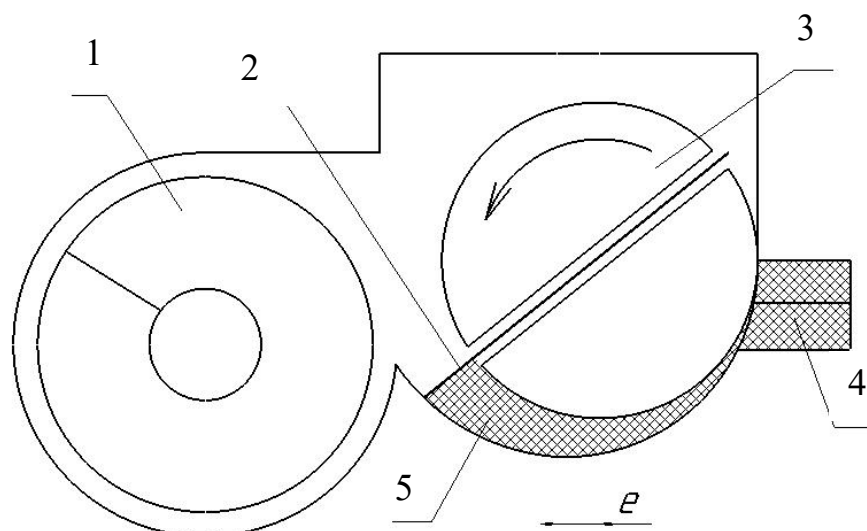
Схема пластинчатого (шиберного) пресса:
